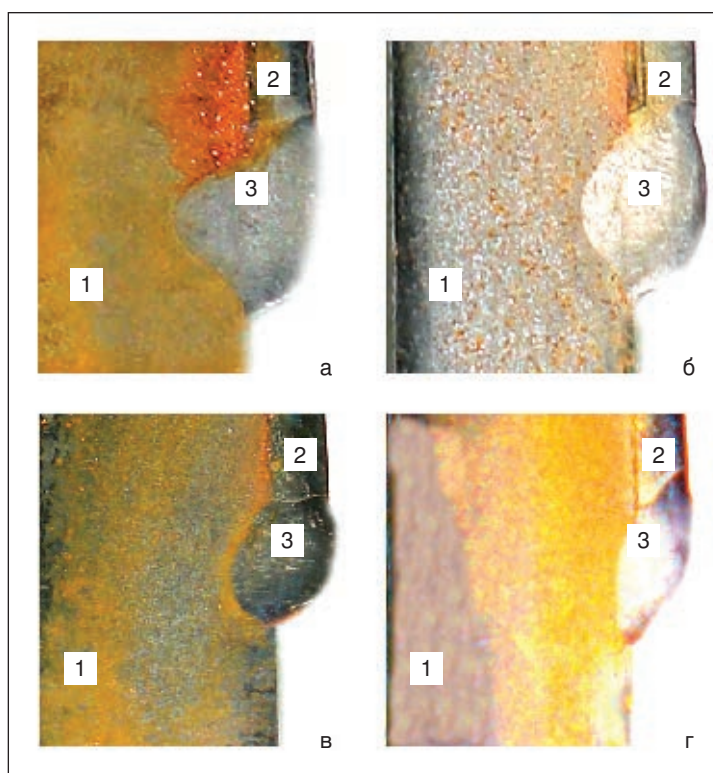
Вид макрошлифов сварного соединения из разнородных сталей 10X13Г18ДУ+09Г2С, сваренных под разными углами наклона сварочной горелки: а — 65° ; б — 55° ; в — 45° ; г — 35° (1 — сталь 09Г2С, 2 — сталь 10X13Г18Д; 3 — сварной шов); $\times 50$
